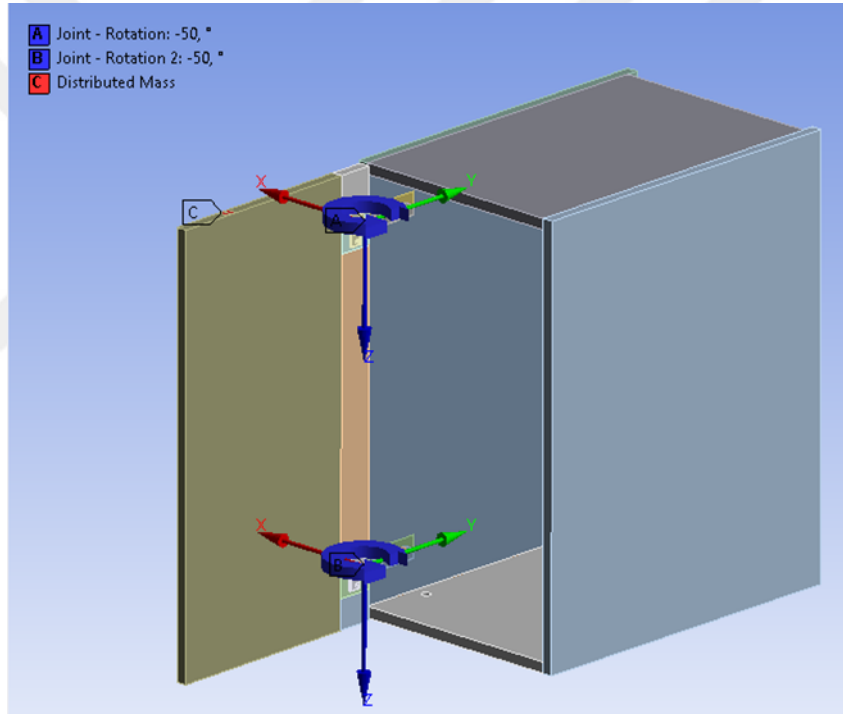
Kapak Test 3 için sınır koşullarının belirlenmesi.
